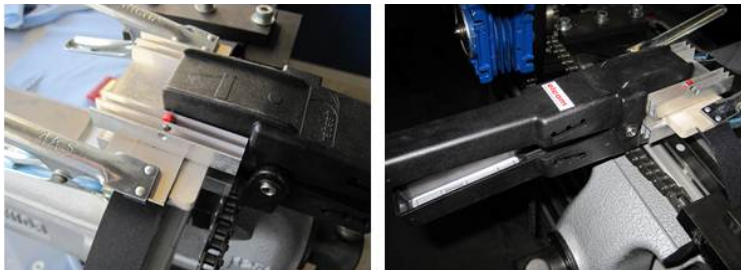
Kühlen der Z-Verbindung nach dem Schweißprozess mit der Kühllange (Art.-Nr.: H080690030)
